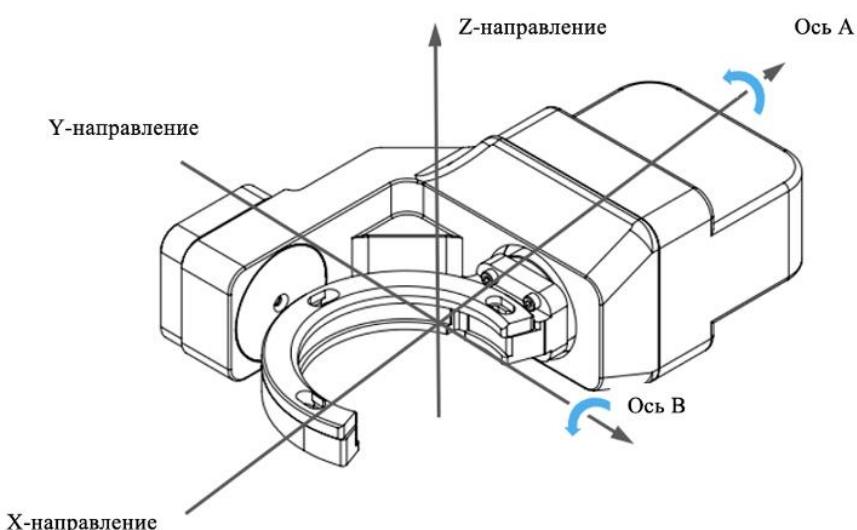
Оси фрезерования и вращения держателя для 5-осевых станков
